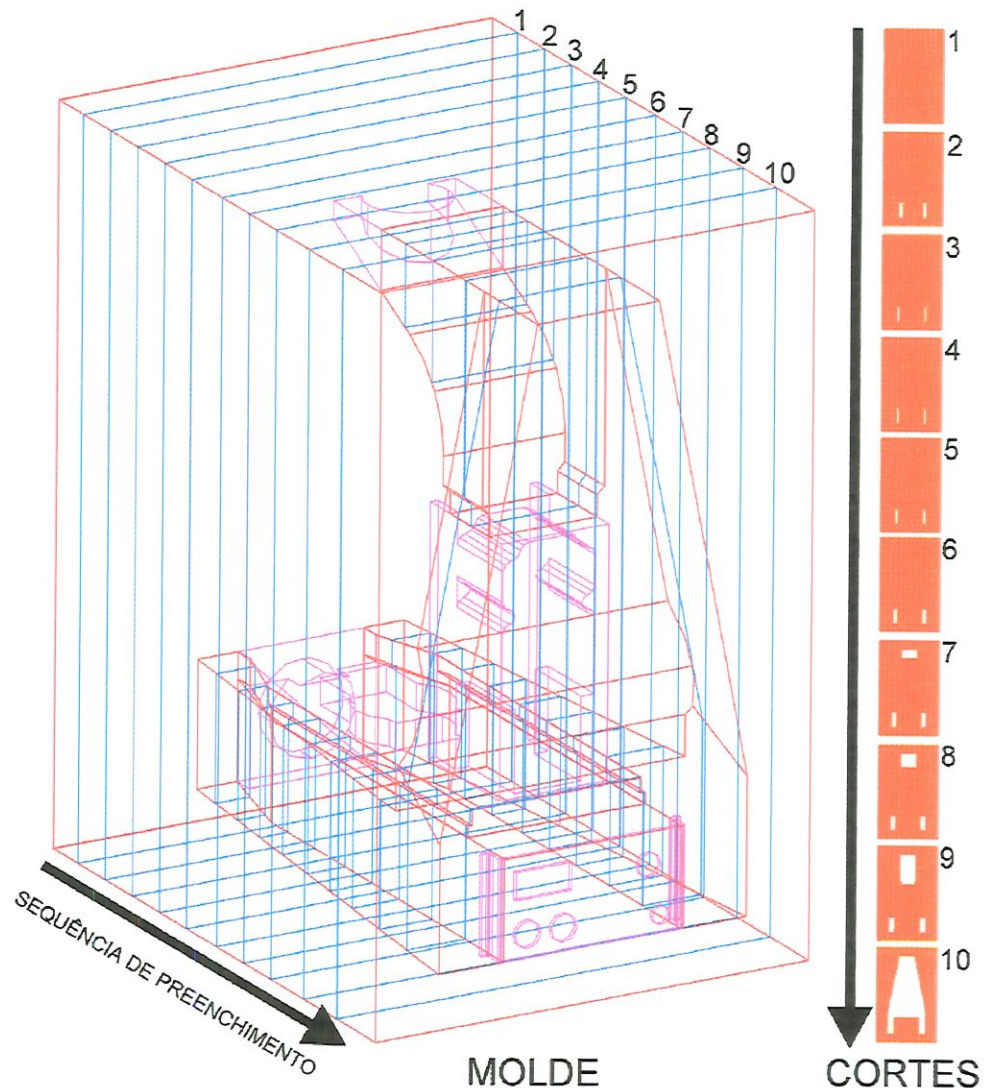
Estudo do caminho percorrido pelo granito sintético durante a moldagem.
